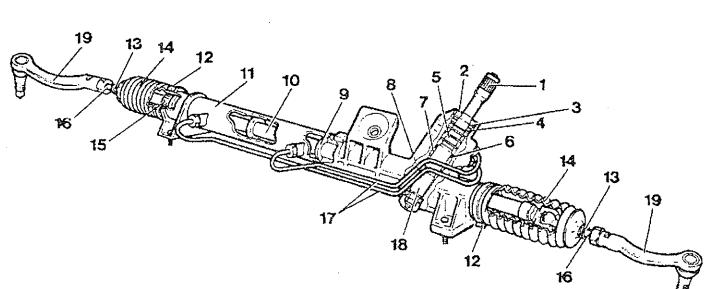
Редуктор рулевого механизма (1 — входящая ось; 2 — защита; 3 — уплотнение; 4 — подшипник; 5 — клапанная катушка; 6 — уплотнение; 7 — подшипник; 8 — поршень; 9 — поршень; 10 — зубчатая рейка; 11 — труба; 12 — зажим; 13 — зажим; 14 — гармошка; 15 — подшипник; 16 — продольная рулевая тяга; 17 — маслопровод; 18 — зубчатый привод; 19 — конец продольной рулевой тяги).
